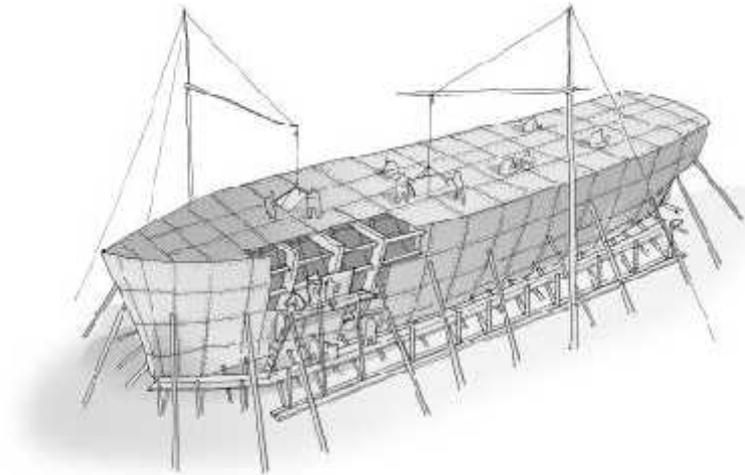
Construcción de un barco por el sistema de remaches.
